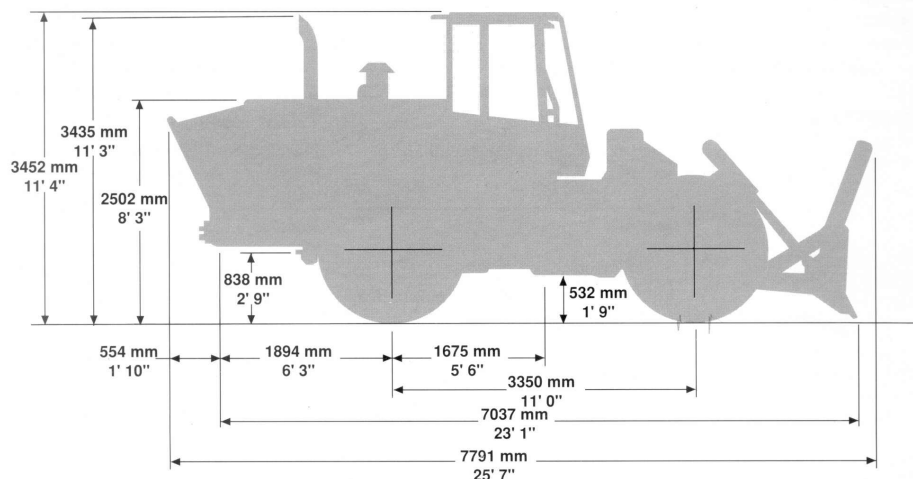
Rolo compactador 816F – Dimensões principais.
